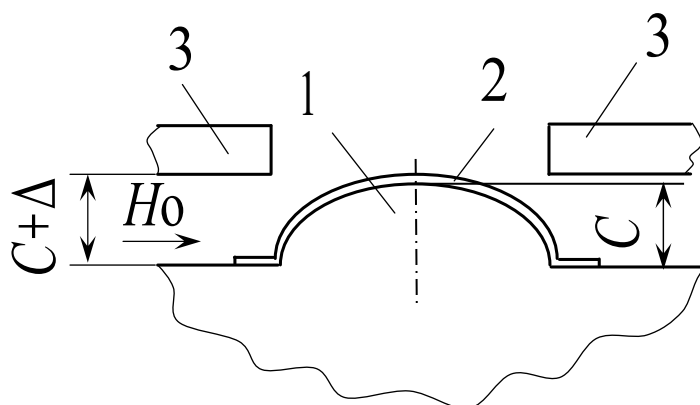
Вид и расположение КМИ при осуществлении способа магнитографического контроля [9]: 1 – контролируемый сварной шов; 2 – магнитная лента; 3 – концентраторы магнитной индукции
